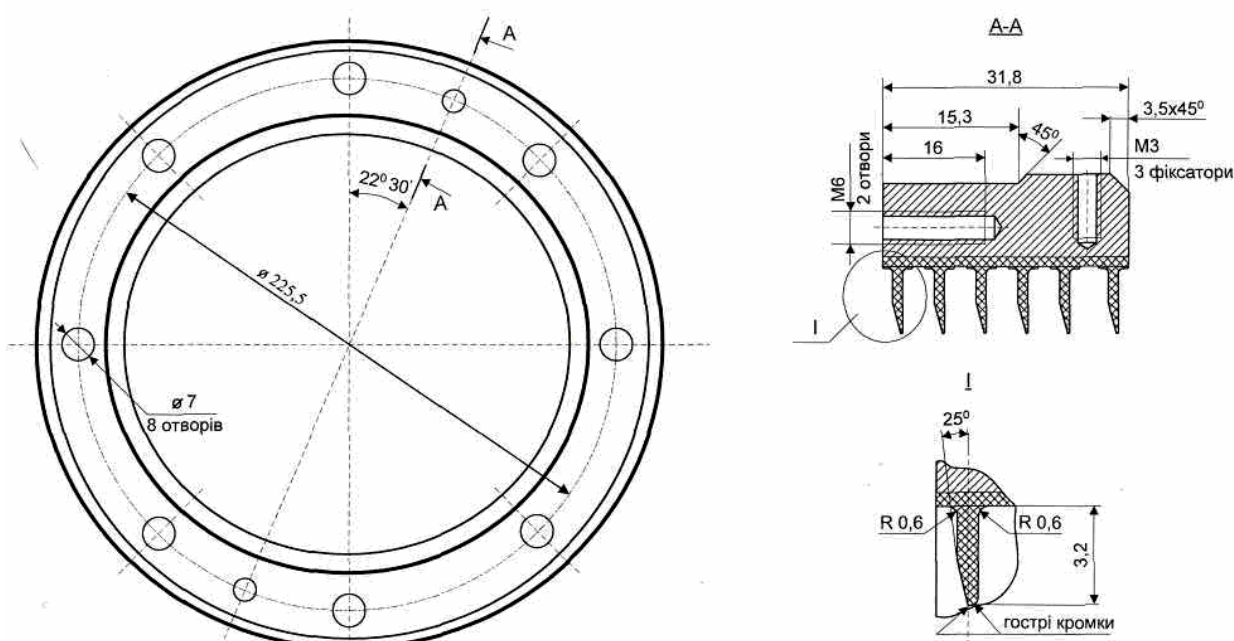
Конструкция уплотнения "масло-газ" из блочного полимерного материала
